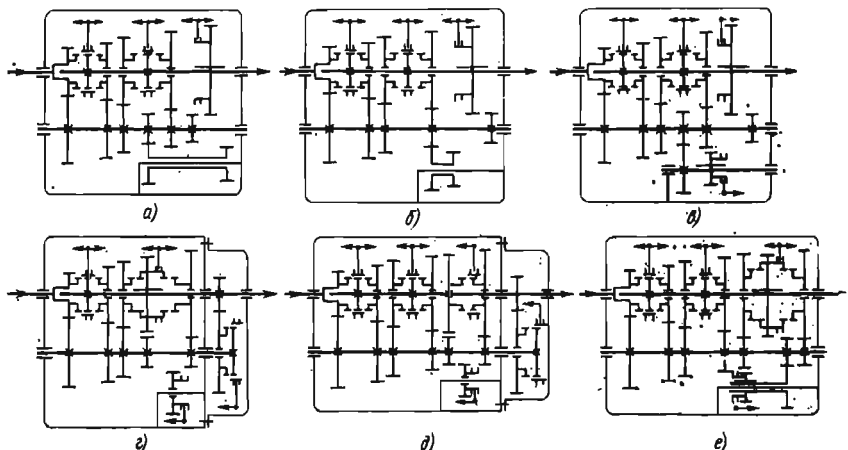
Схемы пяти- и шестиступенчатых соосных коробок передач с передвижным зубчатым колесом:
